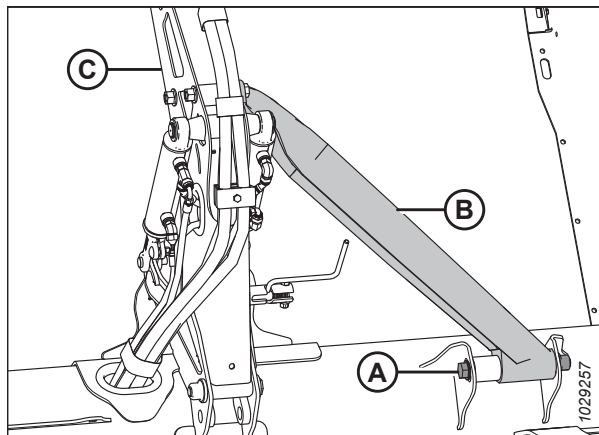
Центральный опорный рычаг сдвоенного мотовила
